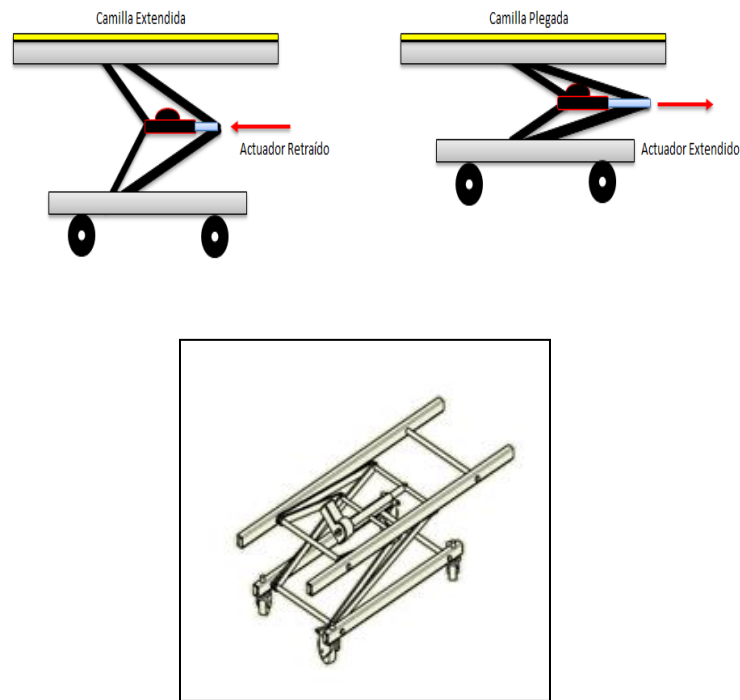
Propuesta N° 1 del sistema de plegado
